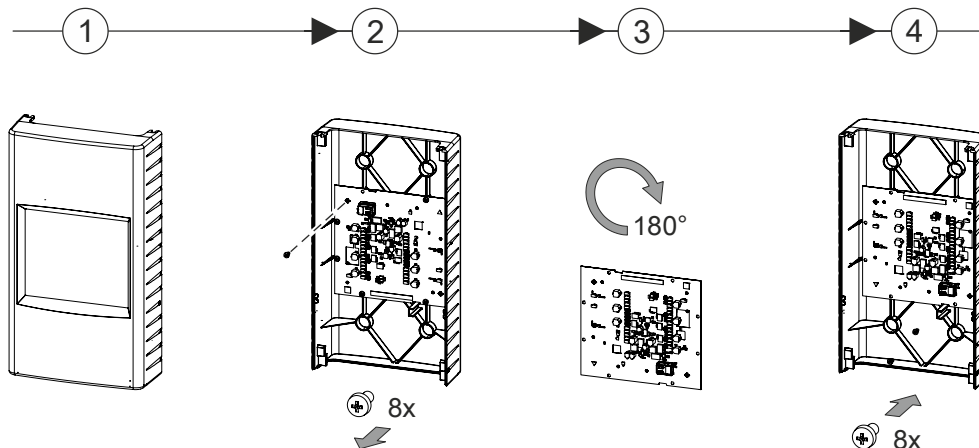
Anpassen der Frontanzeige an die Einbaulage
